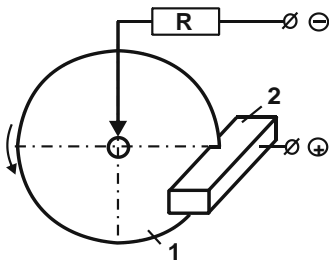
Схема анодно-механічної обробки: 1 – інструмент; 2 – деталь
